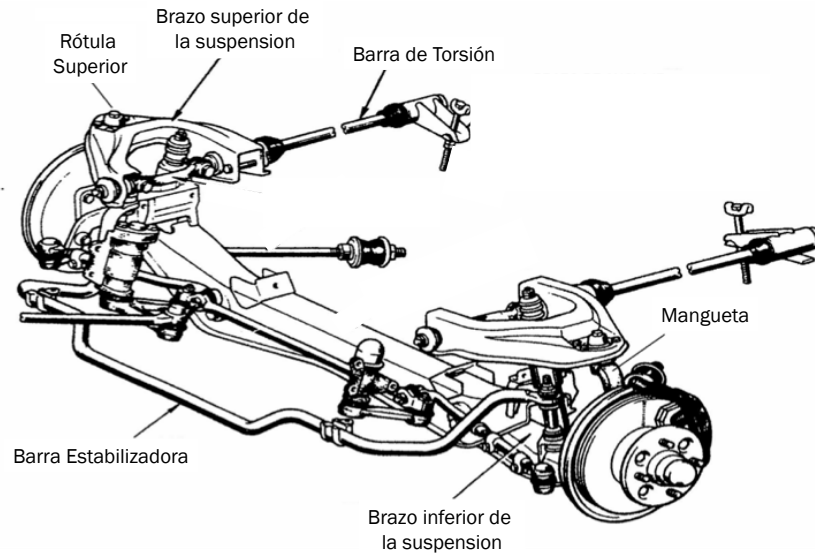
Otros componentes de la suspensión. (SAE Handbook S, 1996)
